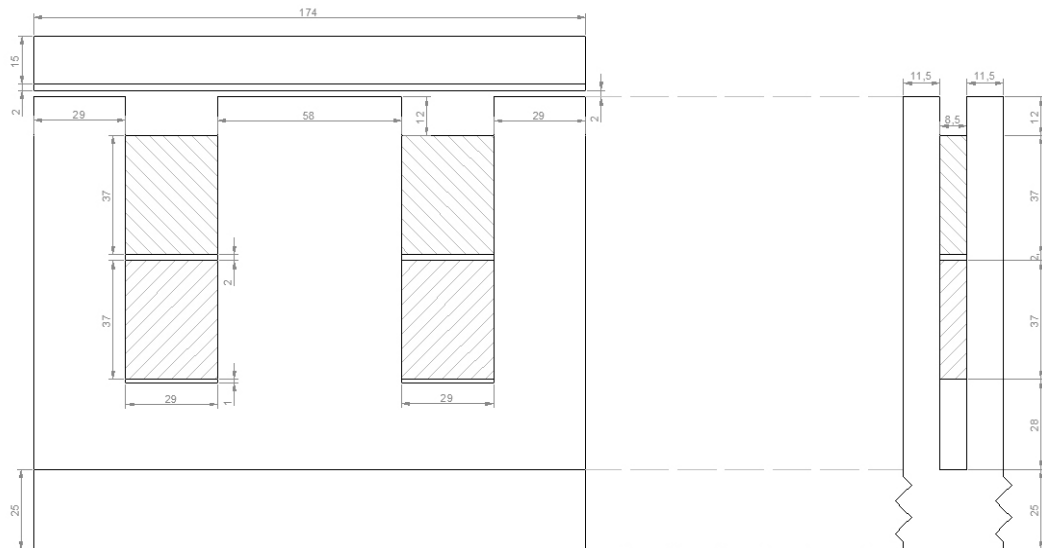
Vista conjunta de sección transversal y longitudinal de la máquina.<sup>[18]</sup>
